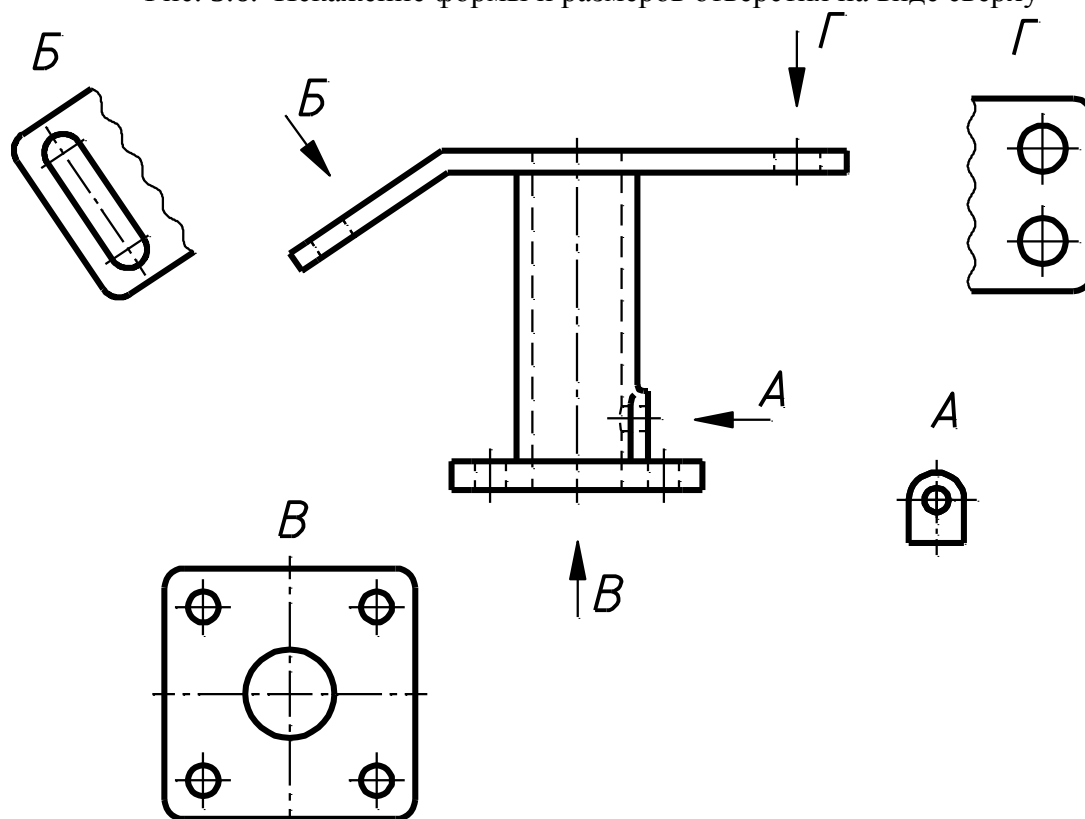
Главный вид (вид спереди), местные виды (вид А, вид В, вид Г) и дополнительный вид (вид Б)
